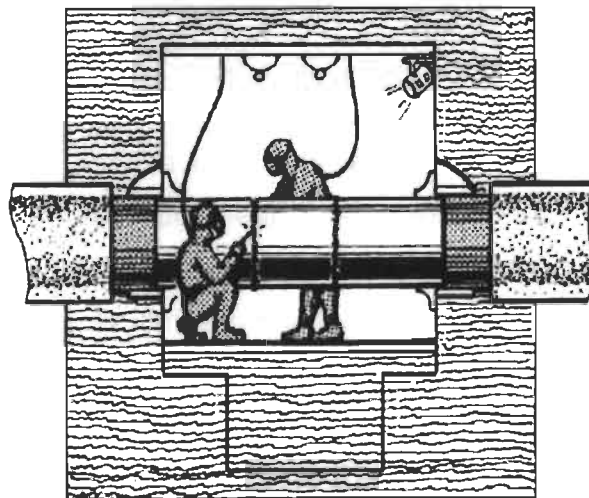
Soldadura submarina en condición seca <sup>[2]</sup>.
